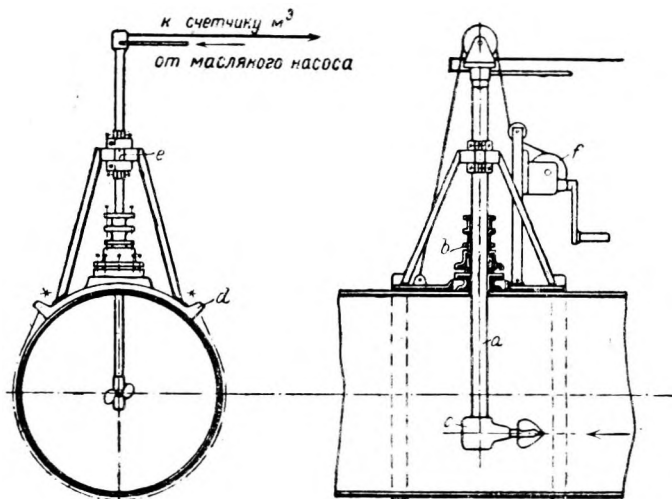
Конструкция для опускания вертушки в напорный трубопровод.
